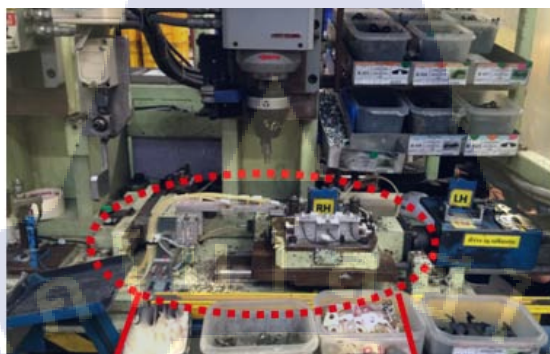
การติดตั้ง Dispenser Valve
